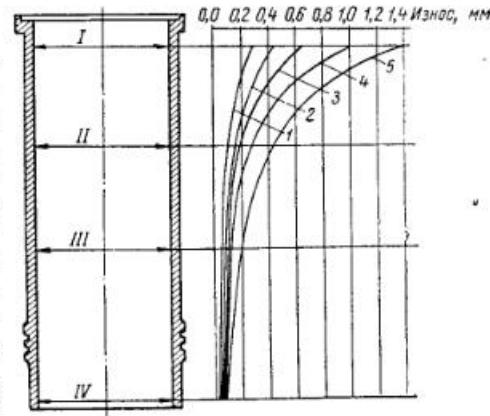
Износ (по диаметру) втулок рабочих цилиндров двигателя 8NVD-36:
